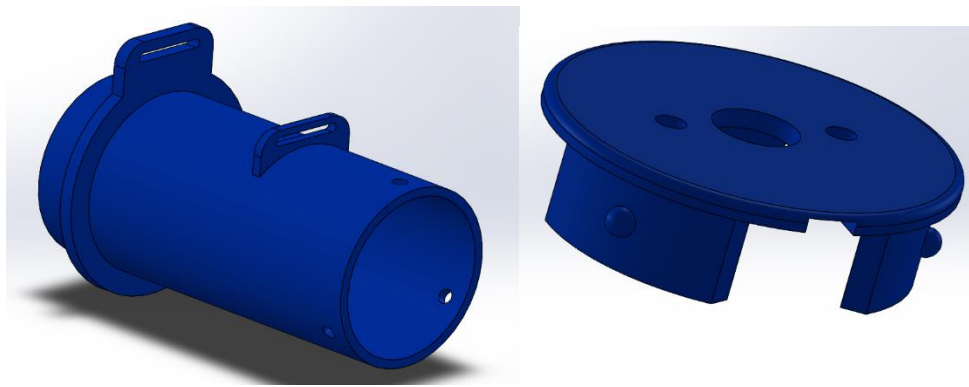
CUERPO DE RETENCIÓN DE MOTOR PARA EFECTOR FINAL
